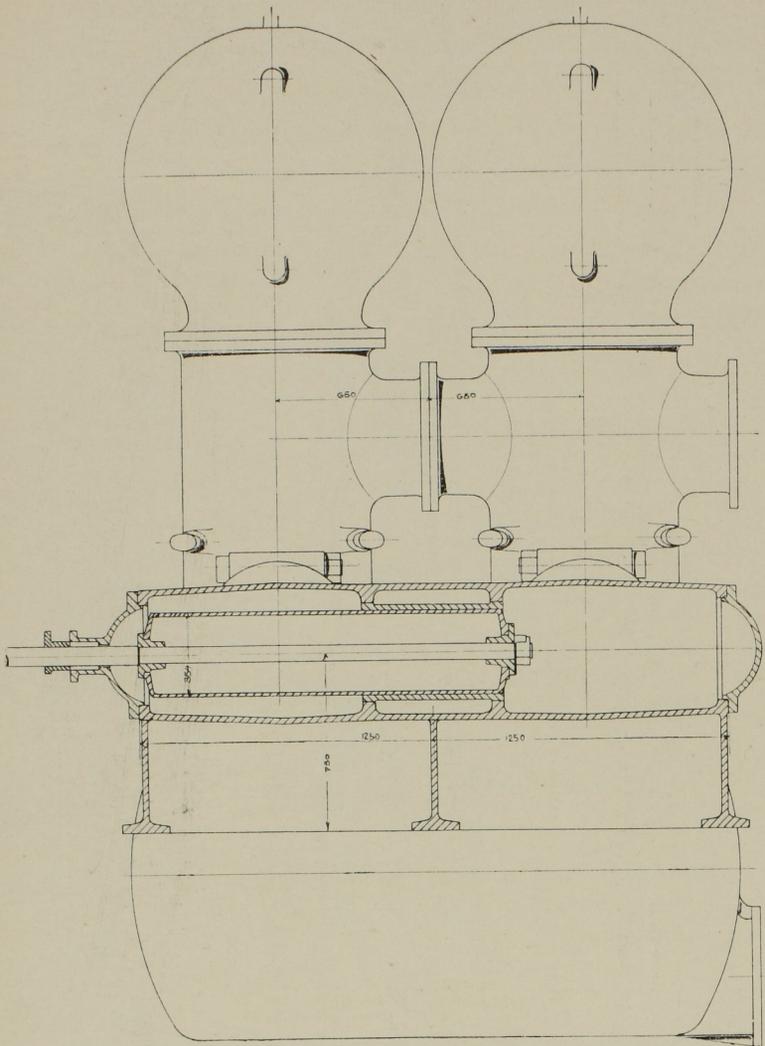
Seitenansicht und Schnitt der Pumpe. Massst. 1:30.
